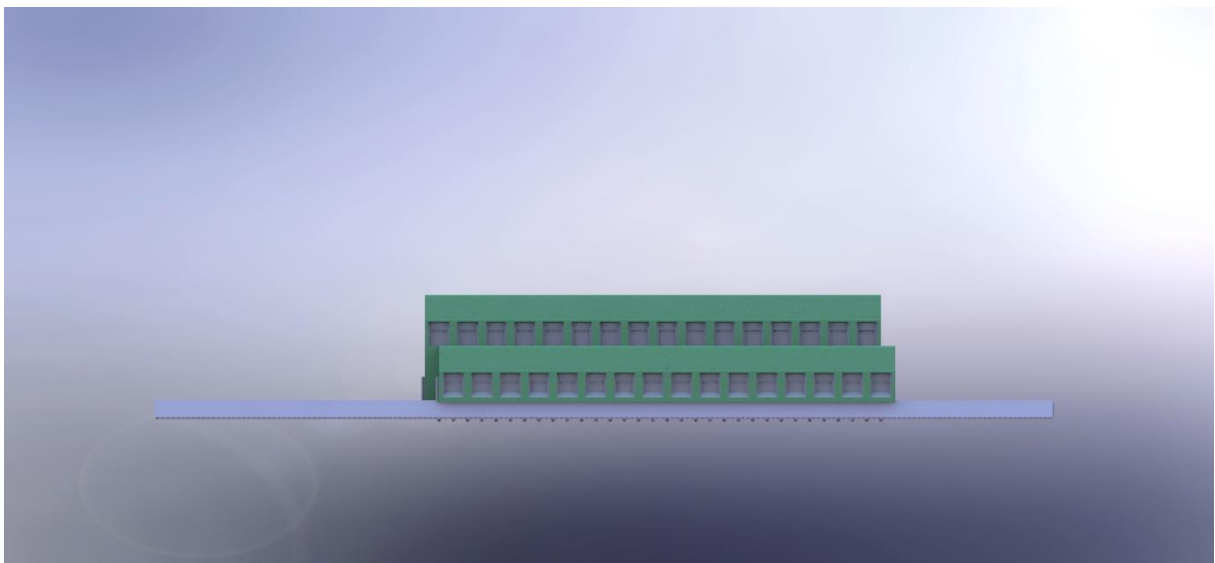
PCB entradas: Vista frontal de la posición de los conectores externos
